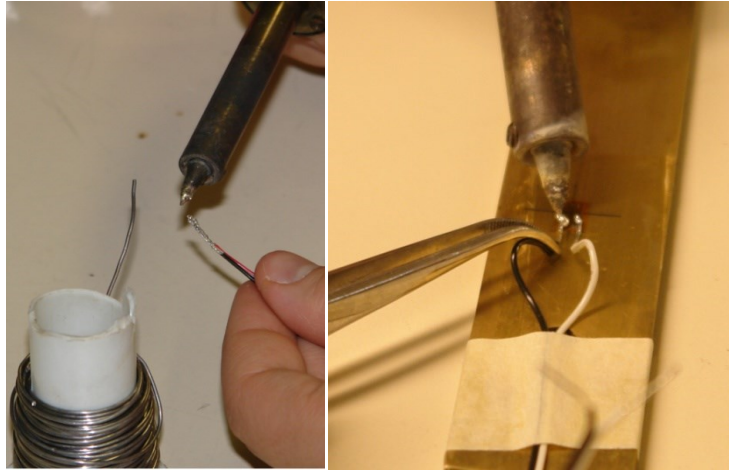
Estañado de los extremos de los cables y soldado a las terminales del extensómetro
